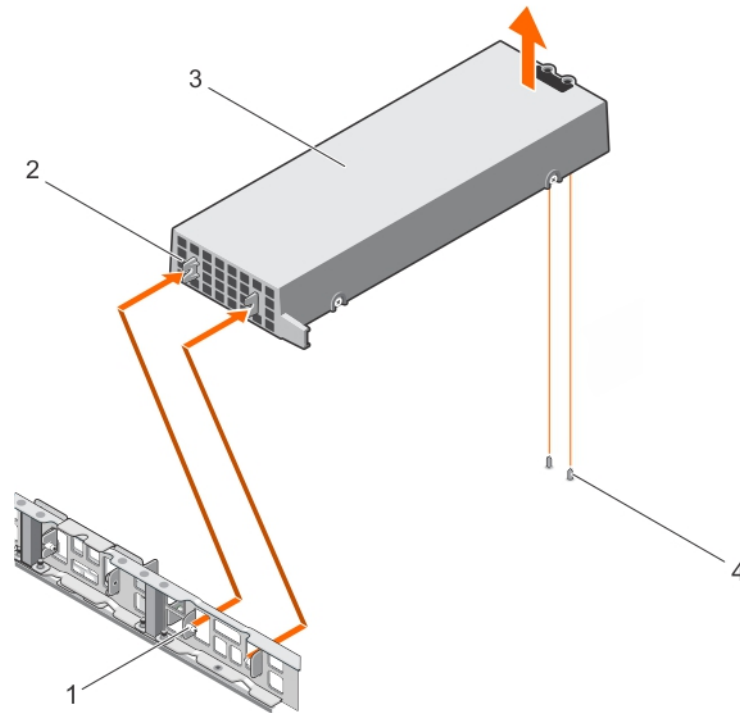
Entfernen einer GPU-Platzhalterkarte
